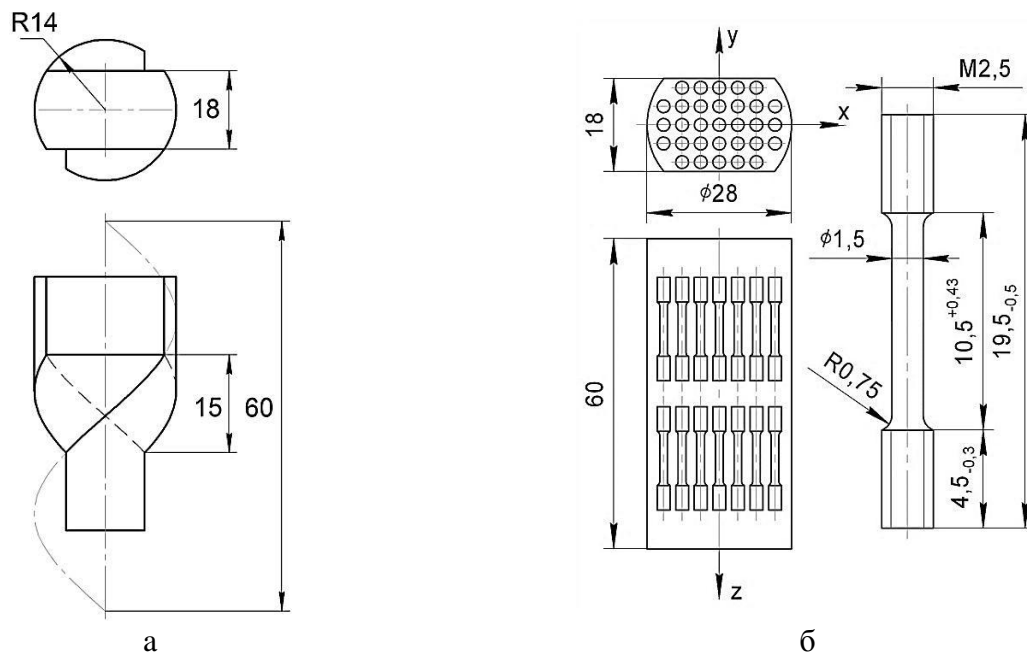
Схема гвинтової матриці для обробки титанових заготовок (а); схема порізки заготовки та карта зразків на розтягнення (б)
